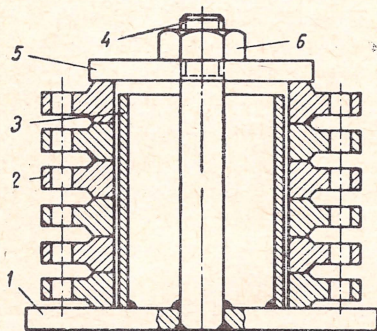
Приспособление для одновременной групповой обработки фланцев
